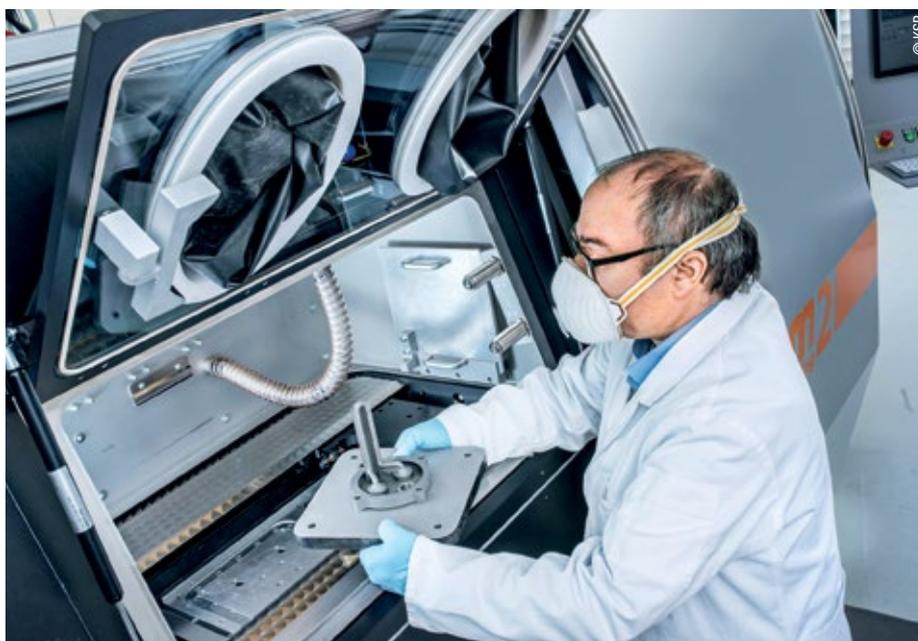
3D-Druck mittels Laserschmelzen wird den Ersatzteilmarkt auch in der Pumpenbranche revolutionieren.
